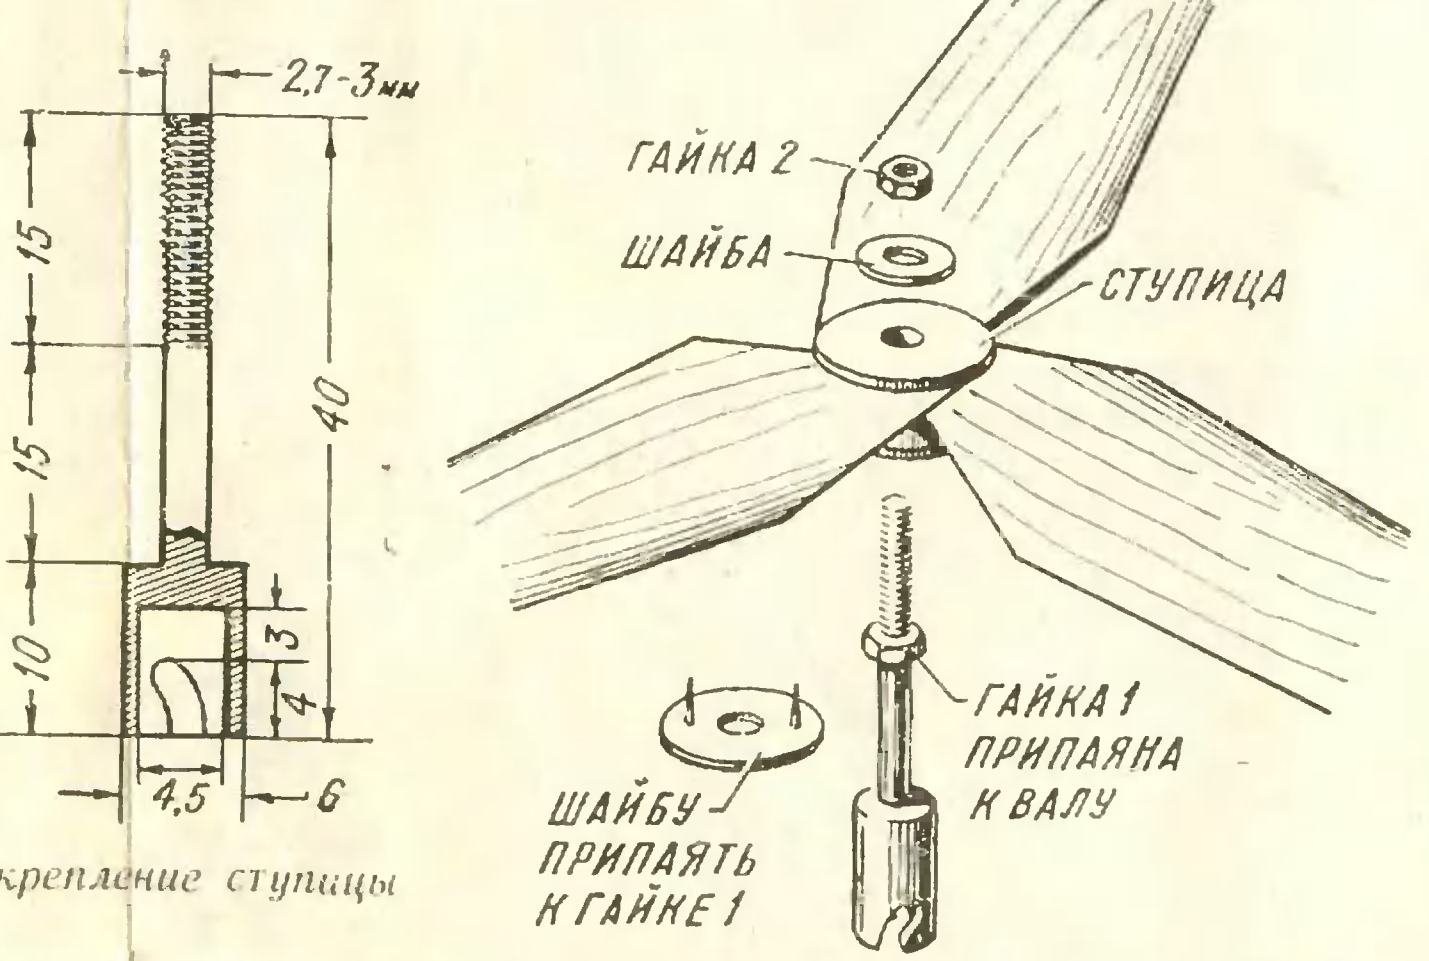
Вал несущего винта и крепление ступицы вертолёта
